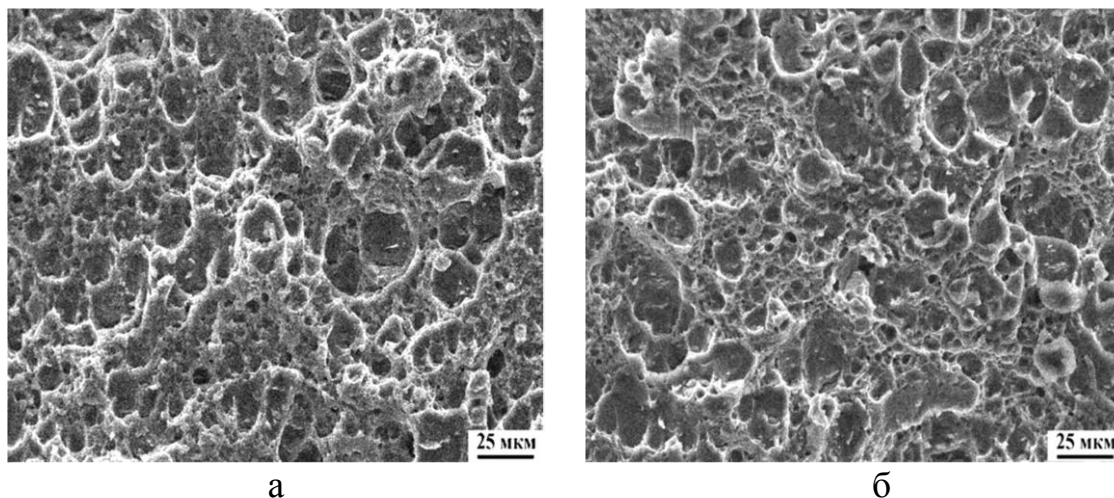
Структура поверхности разрушения металла шва сварного соединения листов сплава 1565ЧН116:
